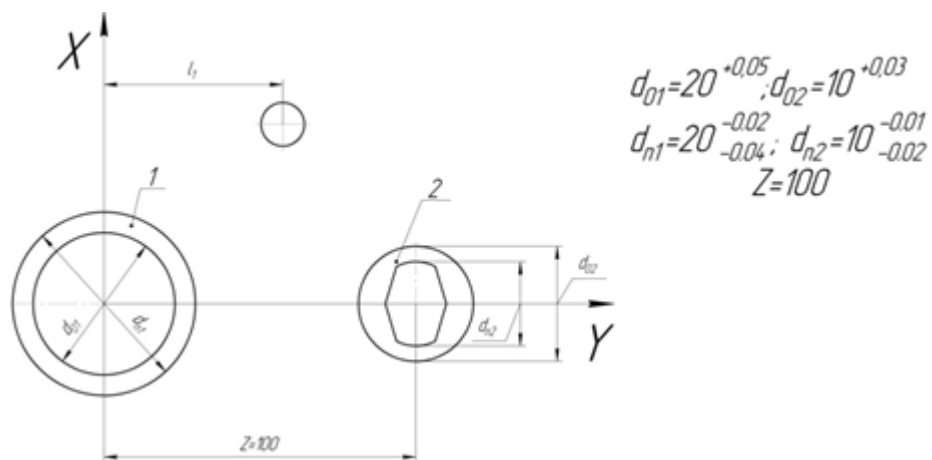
Схема установки детали в приспособлении к заданию 8
